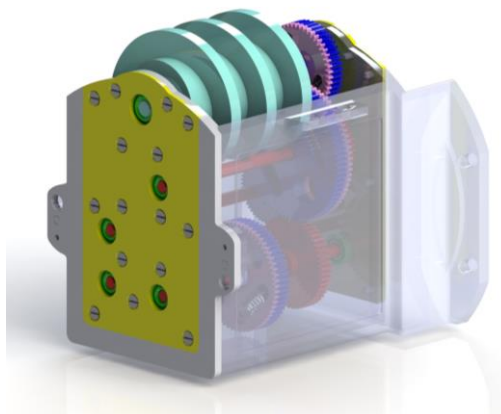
3D модель редуктора, полученная в SolidWorks
